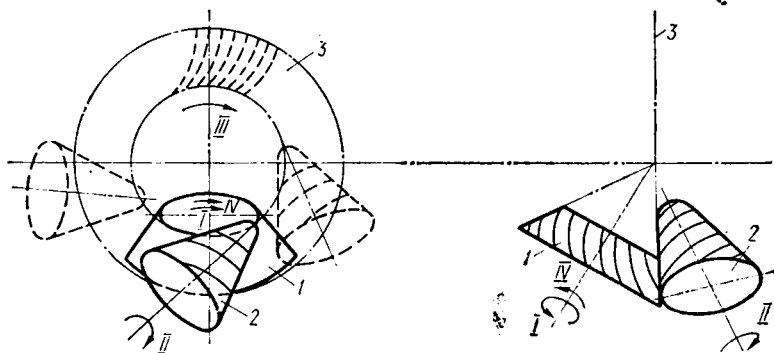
Схема нарезания зубьев паллоидного зацепления червячной конической фрезой
